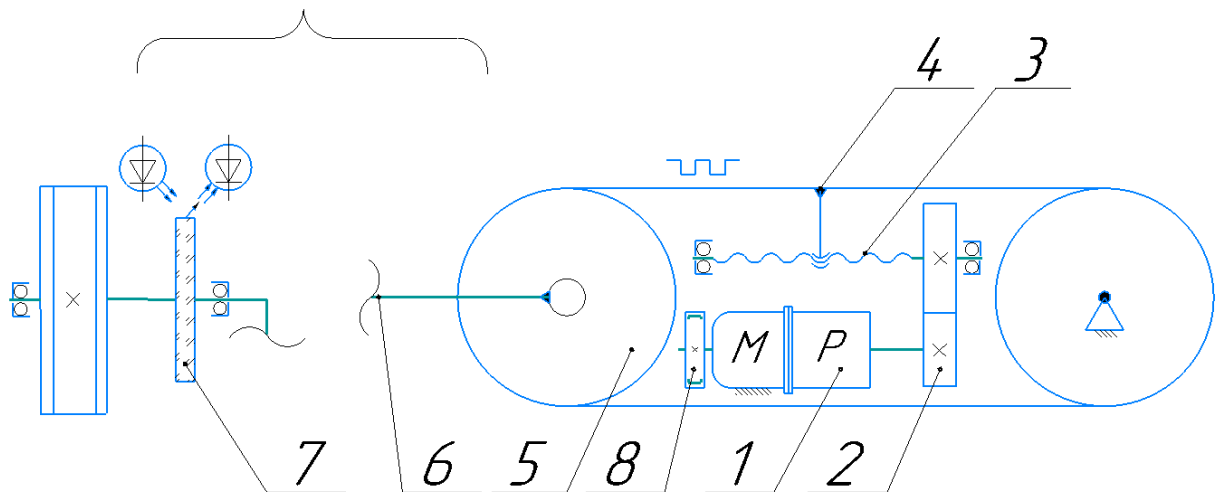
Кинематическая схема привода шарнира
